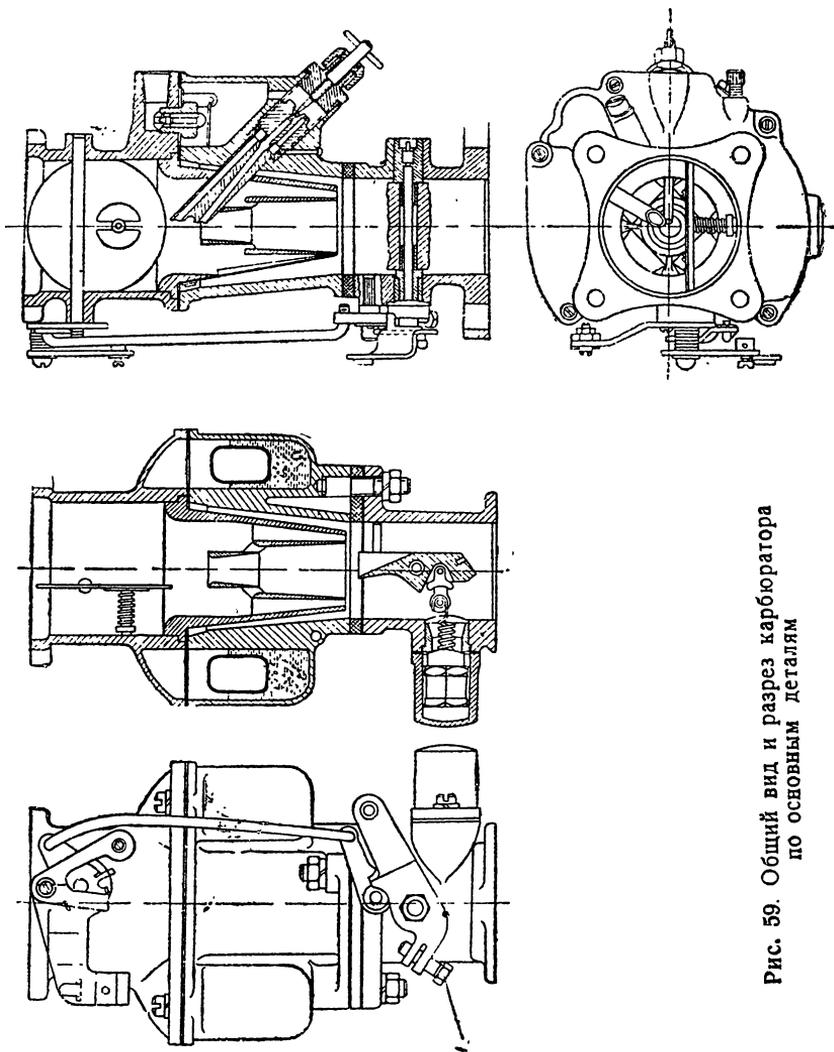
Общий вид и разрез карбюратора по основным деталям
